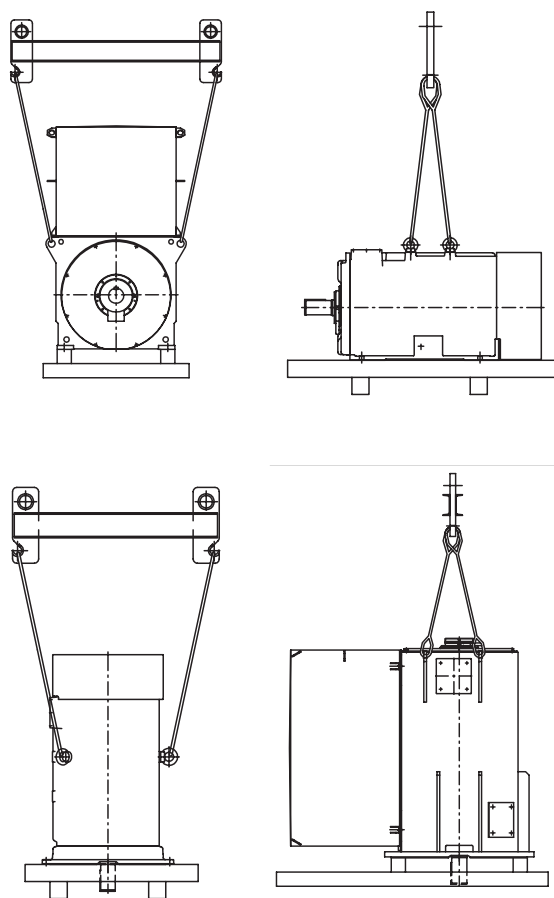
Elevación de máquinas horizontales y verticales en palés
